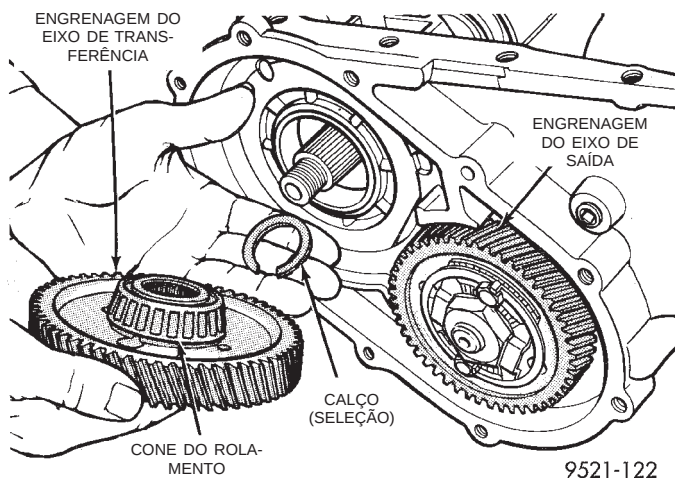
Engrenagem do Eixo de Saída e Calço (Seleção)
